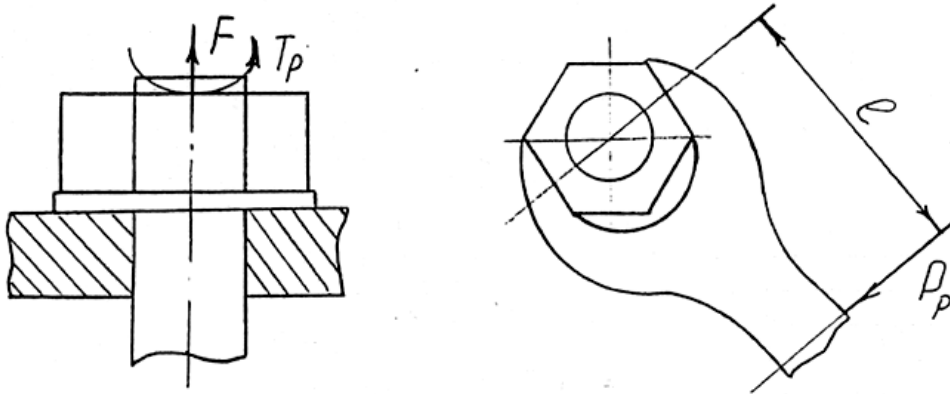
Схема до розрахунку різьбового з'єднання
